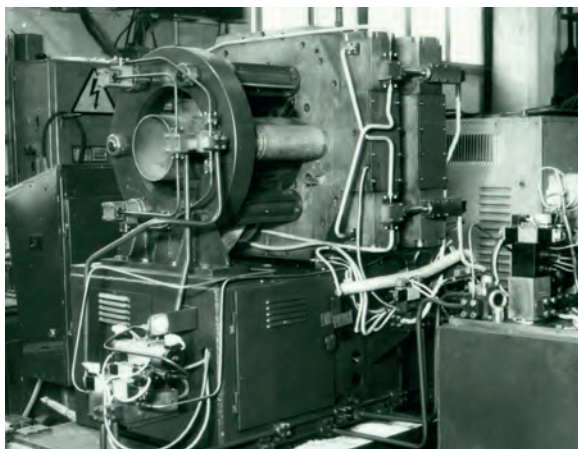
Установка П-145 для індукційного зварювання труб встик діаметром до 12 дюймів
